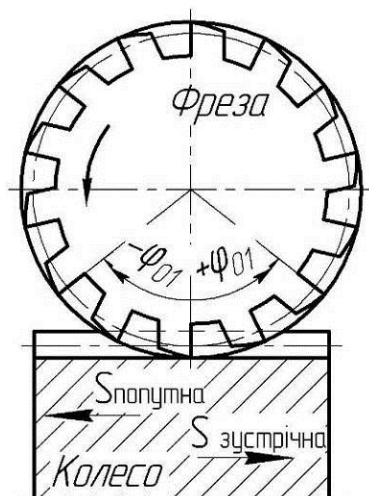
Підрахунок кута повороту фрези при зубофрезеруванні
